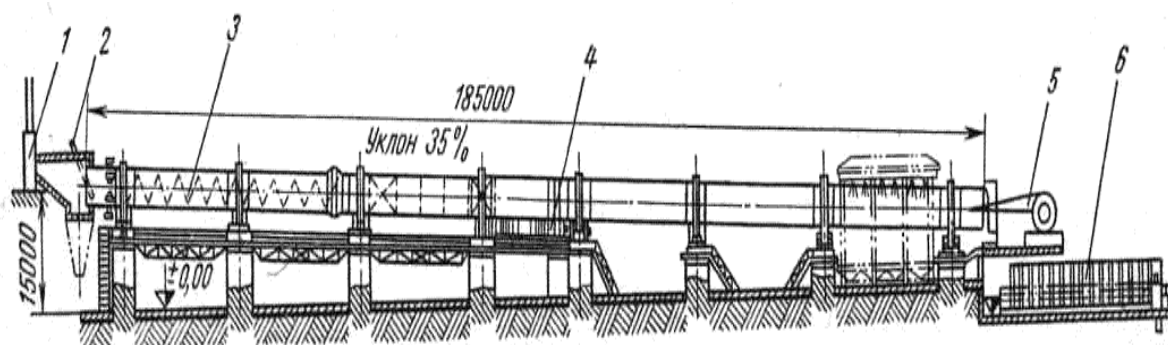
Вращающаяся печь размером 5×185 м: 1 – дымосос; 2 – питатель для подачи шлама; 3 – барабан; 4 – привод; 5 – вентилятор с форсункой для вдувания топлива; 6 – холодильник
